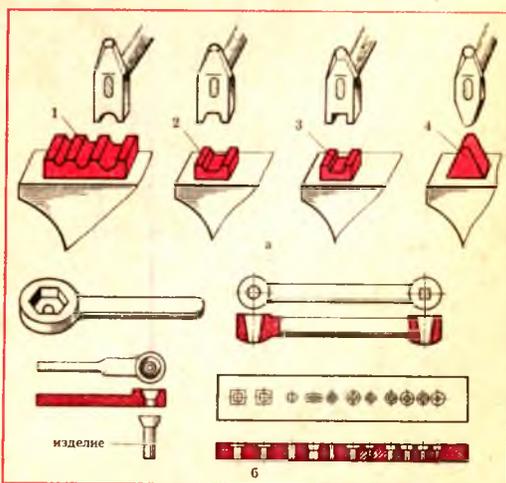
Парный подкладной инструмент: а — обжимки (1—3) и подбойка (4); б — приспособления для высадки гвоздей, болтов, заклепок
